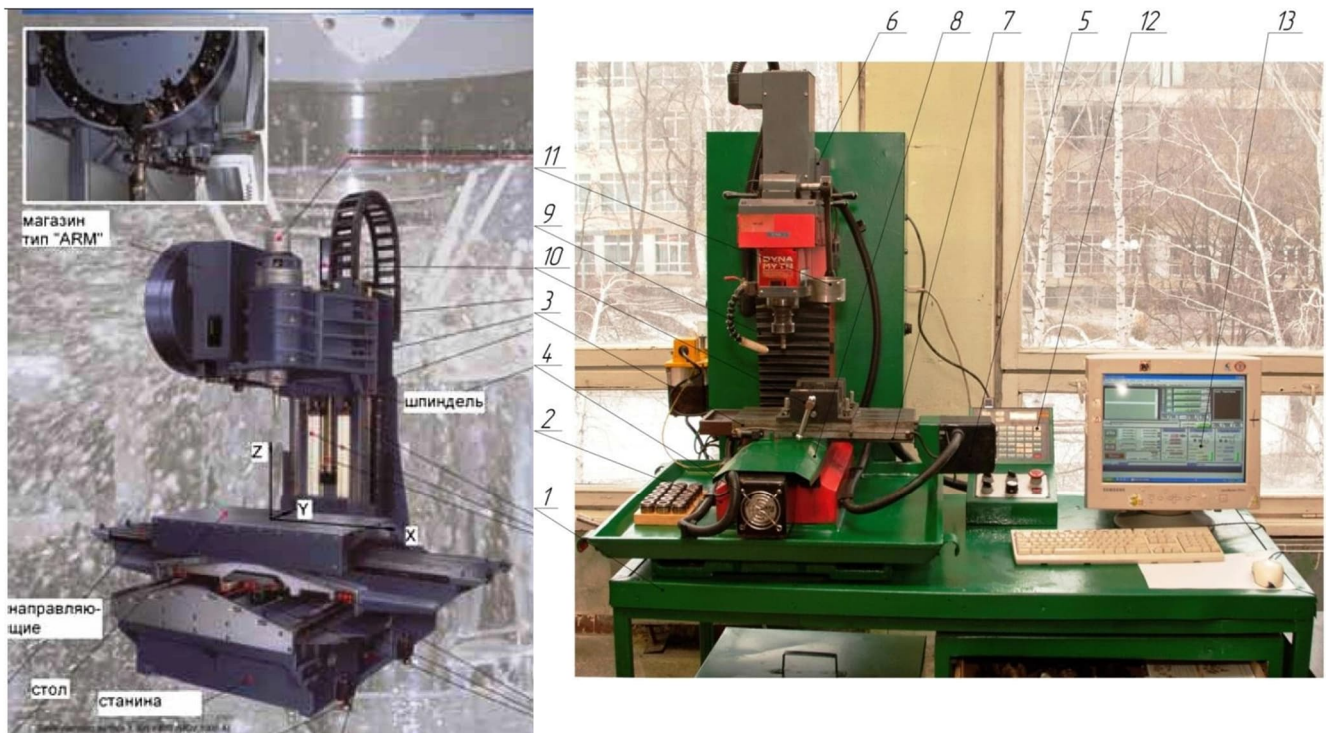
Основні вузли вертикально - фрезерного верстата з ЧПК: 1 – стіл; 2 – станина; 3 – робочий стіл; 4,5,6 – крокові електродвигуни; 7,8,9 – полозки для повздовжнього, поперечного і вертикального переміщення; 10 – лещата; 11 – спеціальний пристрій; 12 – пульт керування; 13 – ЕОМ
